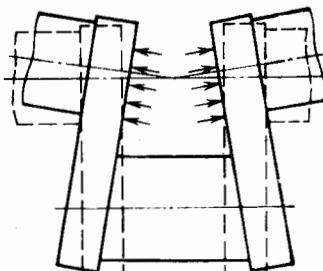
Приспособление для обжима конусного отверстия в рулевой сошке:
